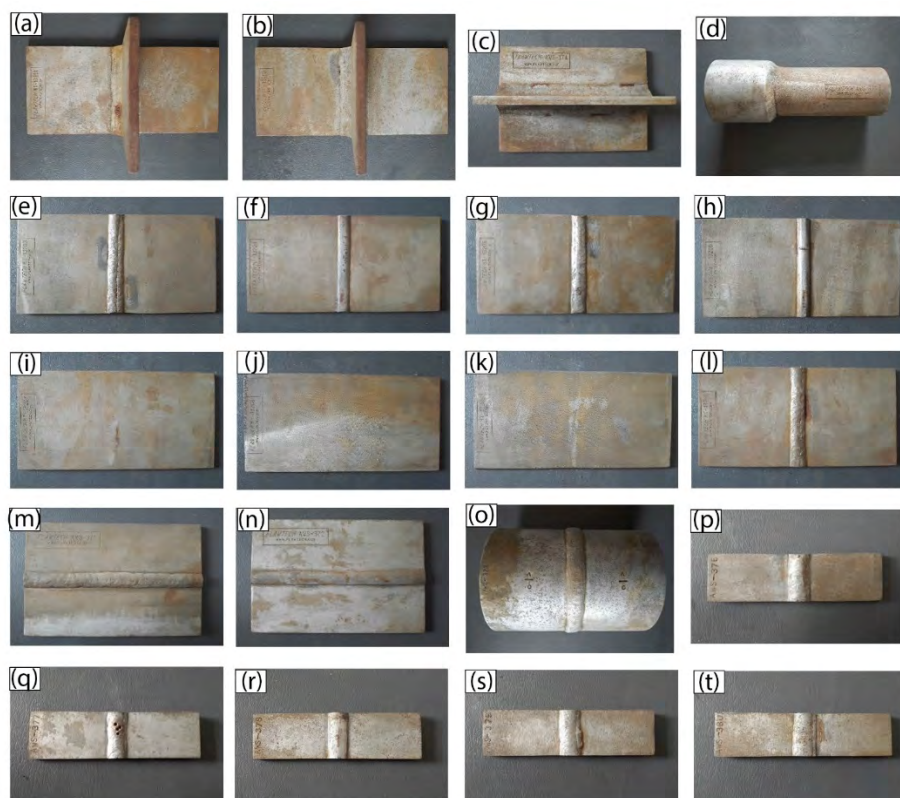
(a-d) soldadura de fillet y (e-t) soldadura de ranura
